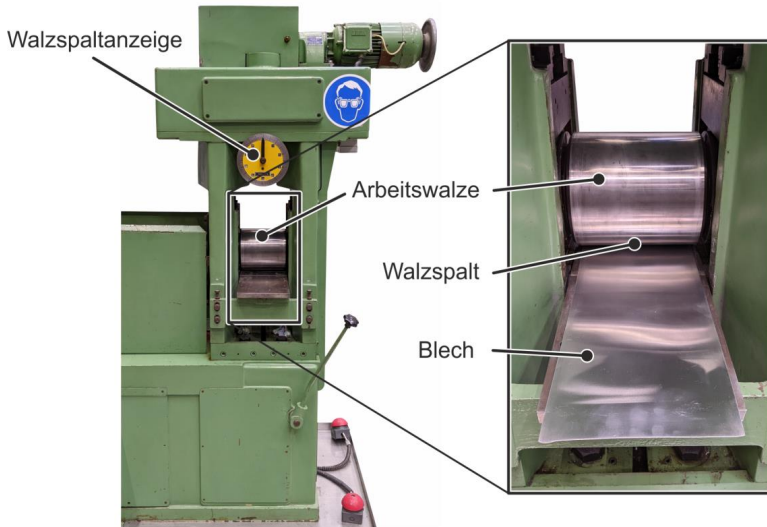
Blechwalzwerk mit zwei Arbeitswalzen zum Aufweiten und Walzen
